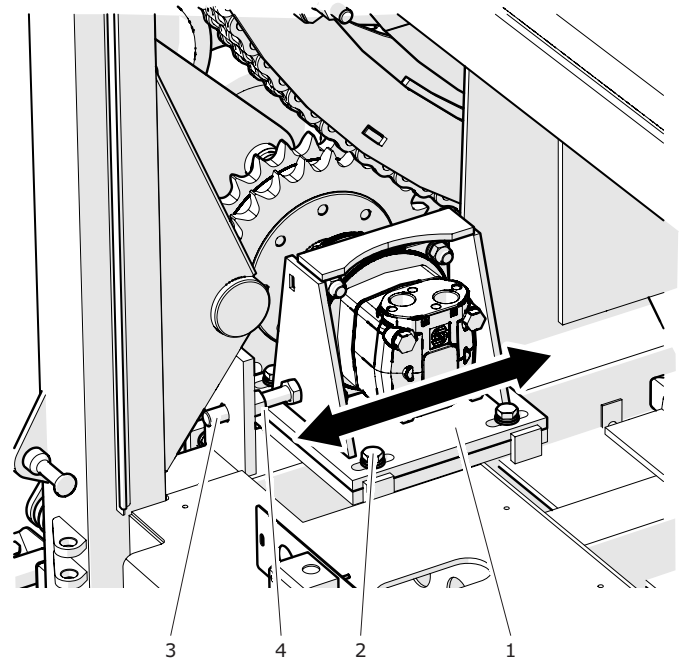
Réglage du positionnement de la roue d'entraînement
